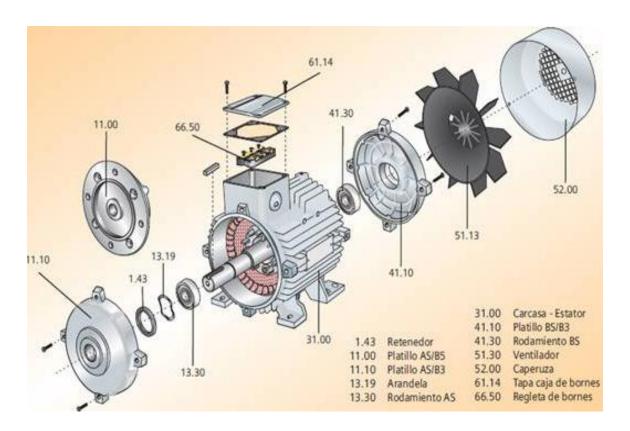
Motor Trifásico 1LA7 080-4YA60 y sus Partes Fuente: http://www.siemens.com.co/SiemensDotNetClient\_Andina/medias/PDFS/17.pdf
